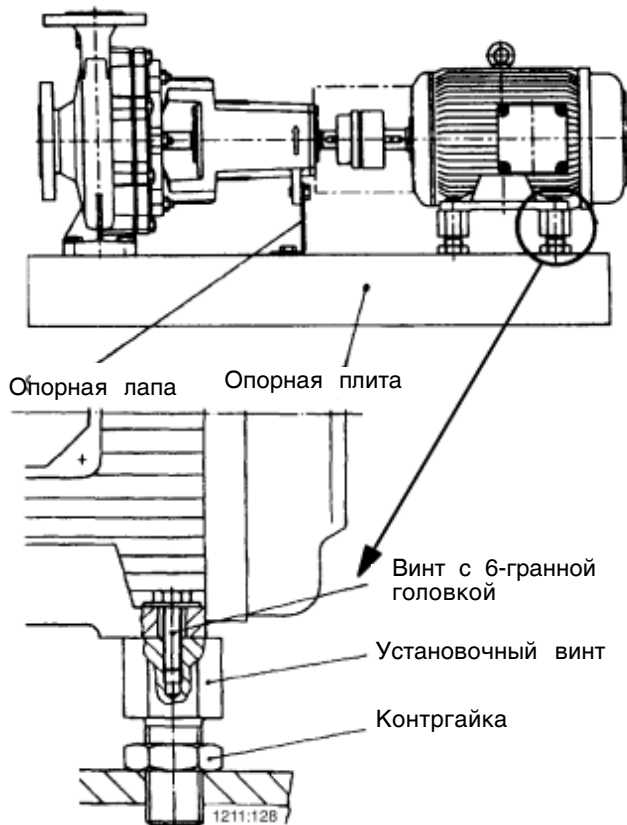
Центровка двигателя посредством установочных винтов
